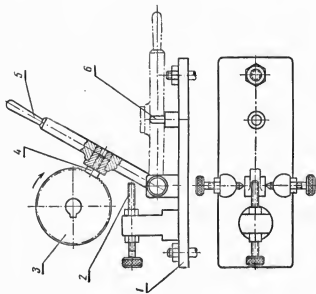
Приспособление для фрезерования шпилек в головках винтов:
